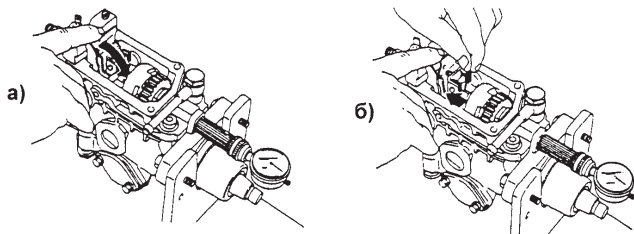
Установочный размер стрелочного индикатора для измерения размера "MS".
